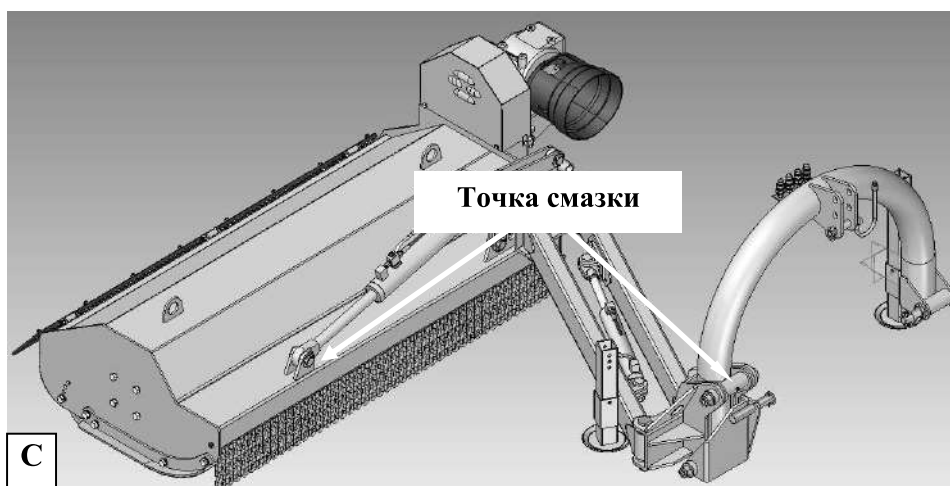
Точки смазки подшипников и шарниров смазкой STP
